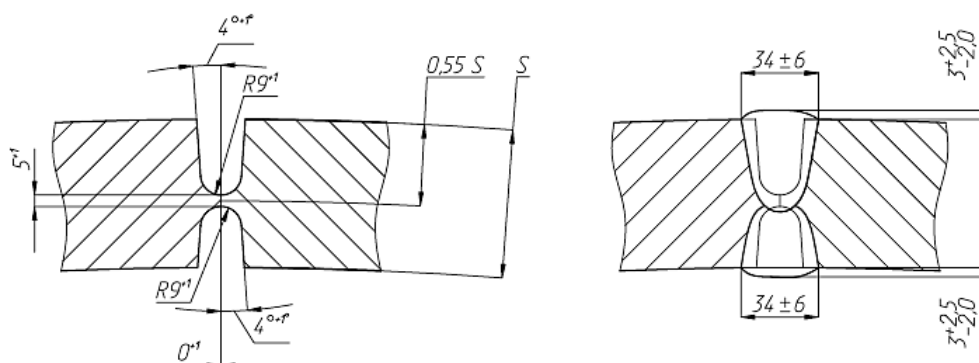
а) разделка кромок под сварку с углом $4^{\circ \pm 1^{\circ}}$, б) выполненное сварное соединение
